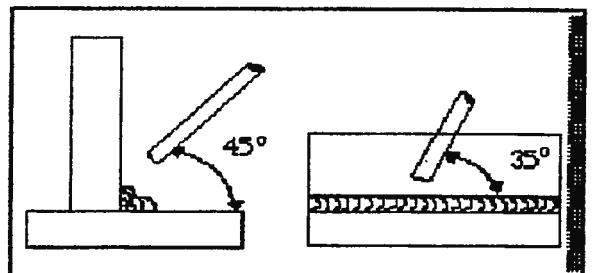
Todas las pasadas apoyadas en la placa vertical
